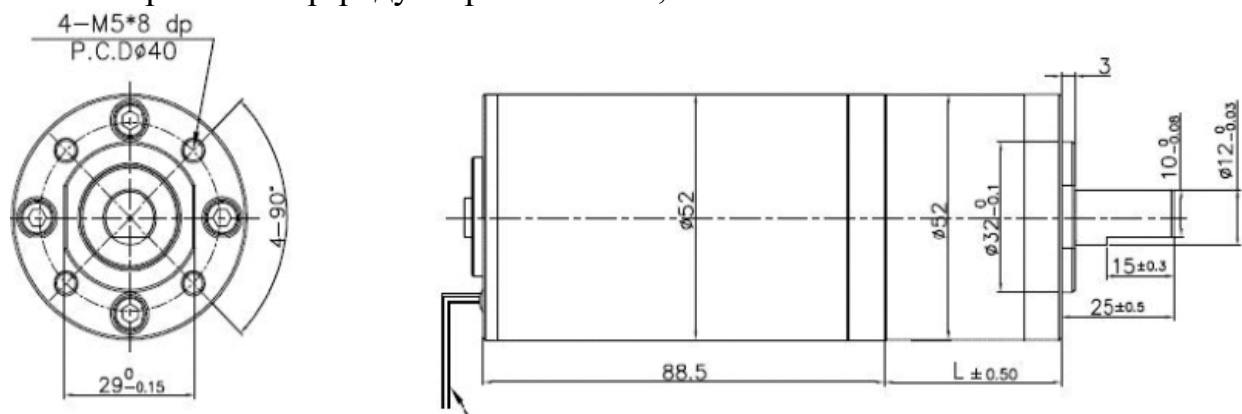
Габаритные и присоединительные размеры мотор-редуктора
